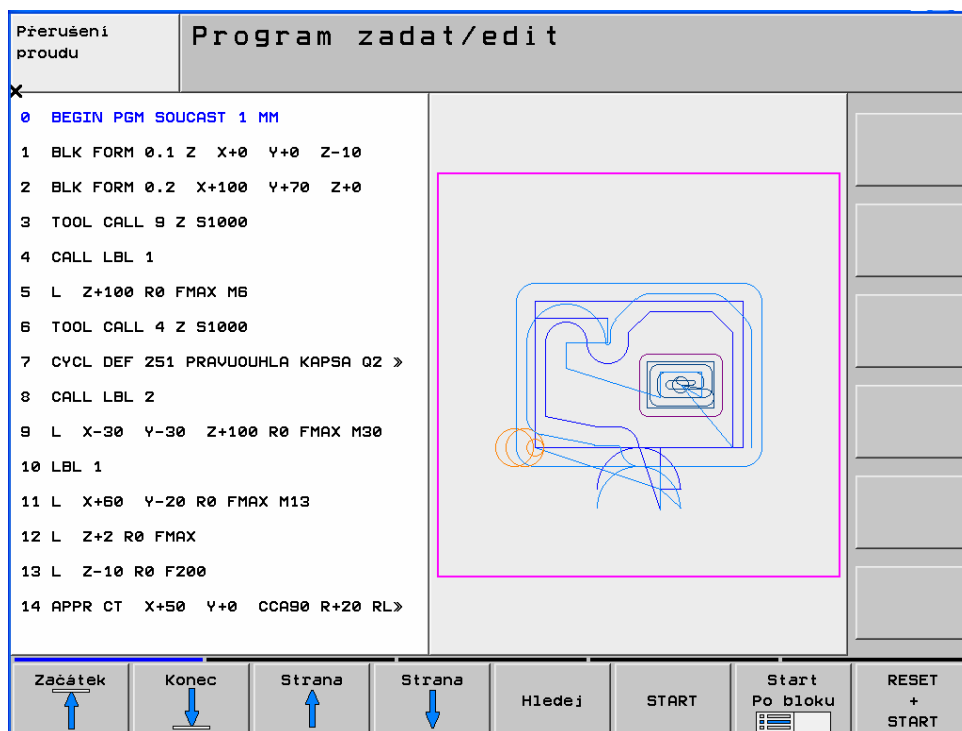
Nástroj pojíždí vpravo od obrysu
